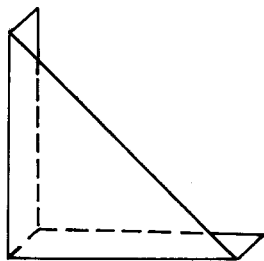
Equerre à joue (hauteur : 6 cm)
